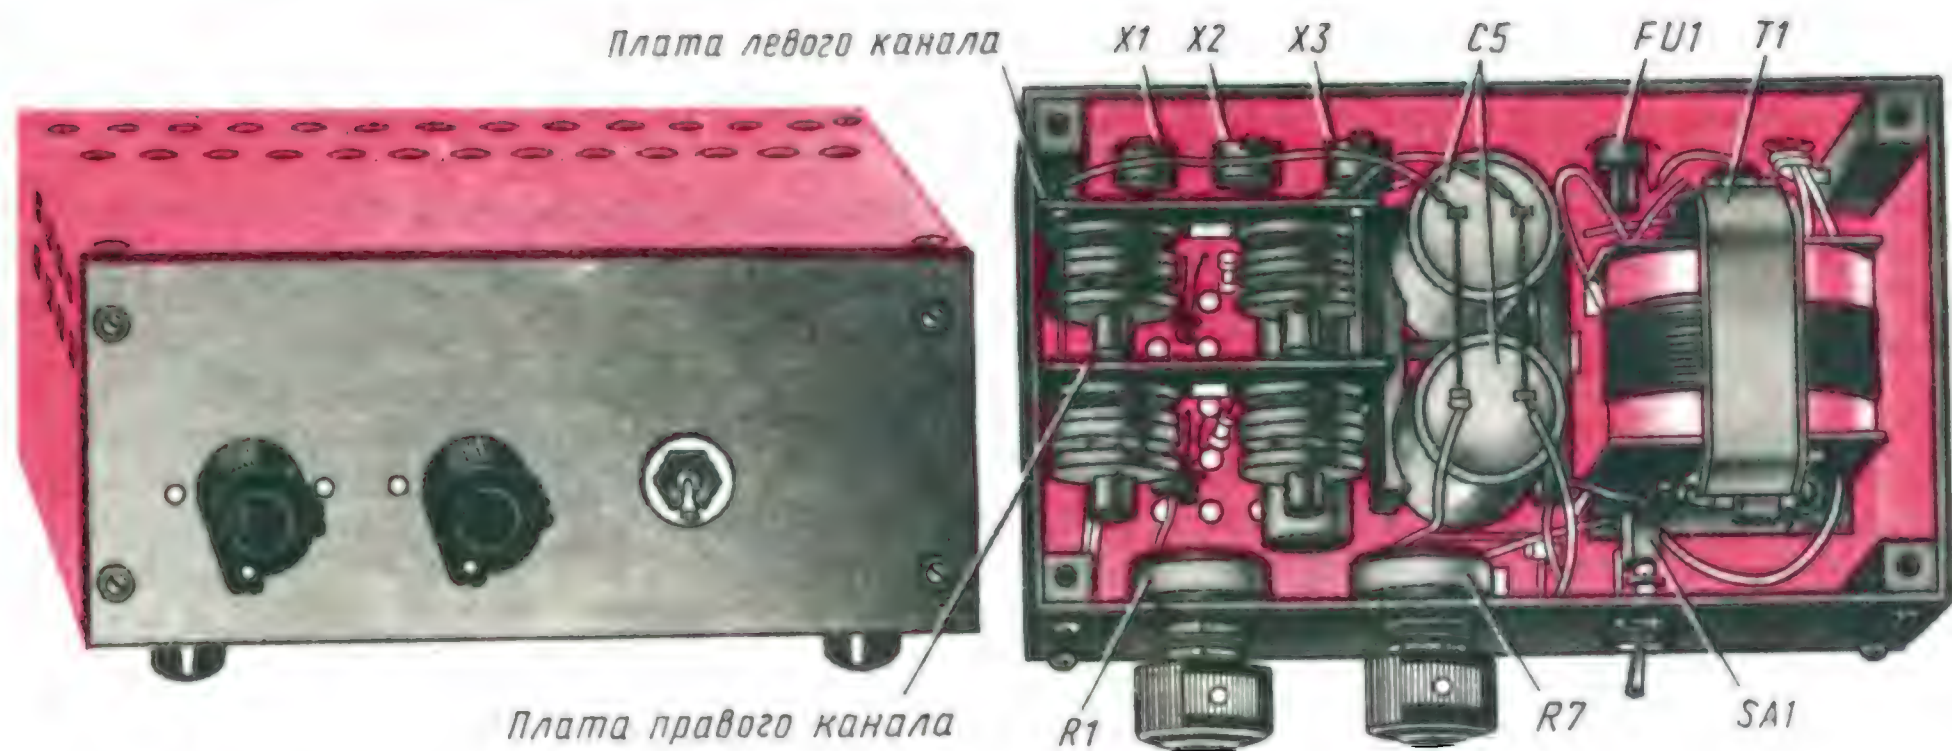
Внешний вид усилителя и размещение деталей в его корпусе (вид сверху)
